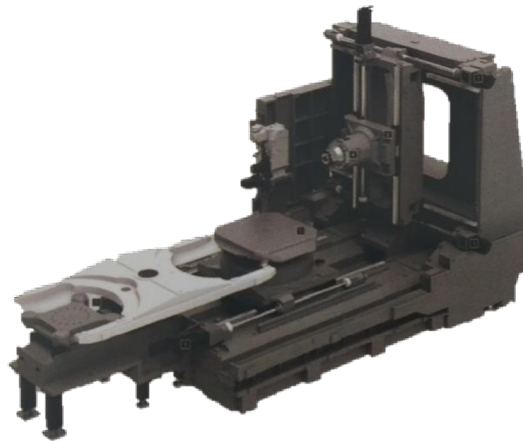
Rozdělení CNC obráběcích center na nerotační součásti [1]
